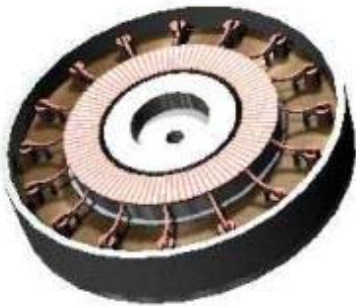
Impulsmagnetisierwerkzeug mit gleichgroßen Polen
